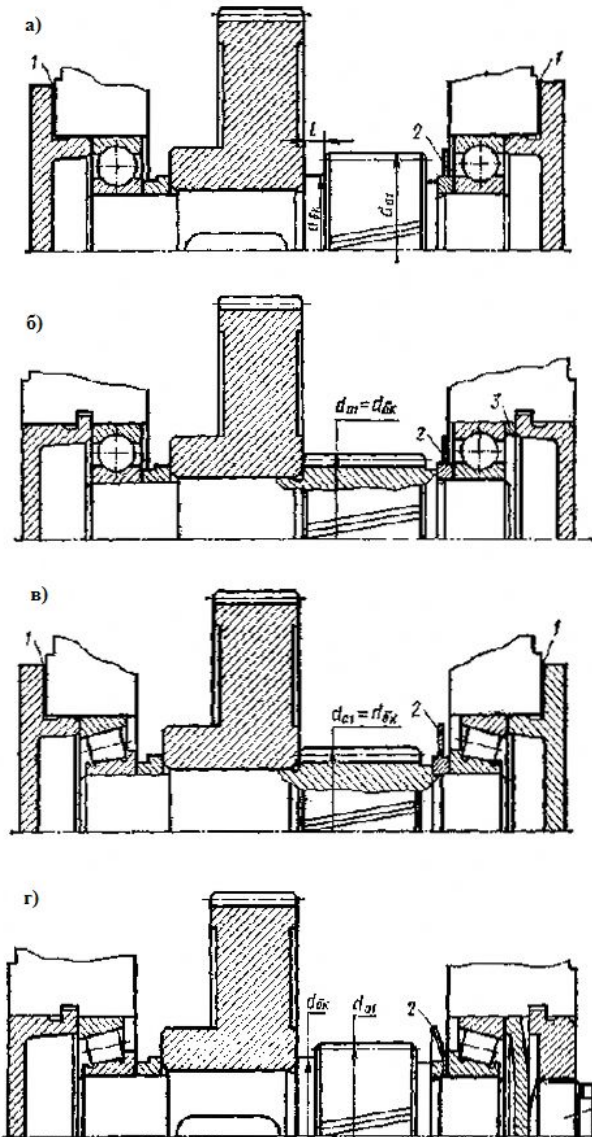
Примеры конструкций промежуточных валов 2-ступенчатого цилиндрического редуктора
